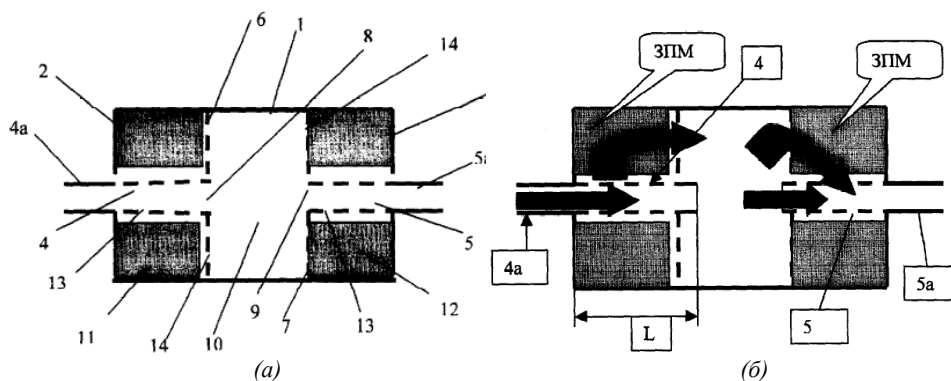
Вариант конструктивного исполнения трехкамерного глушителя шума (а), принципиальная схема передачи через него звуковых колебаний (б):
